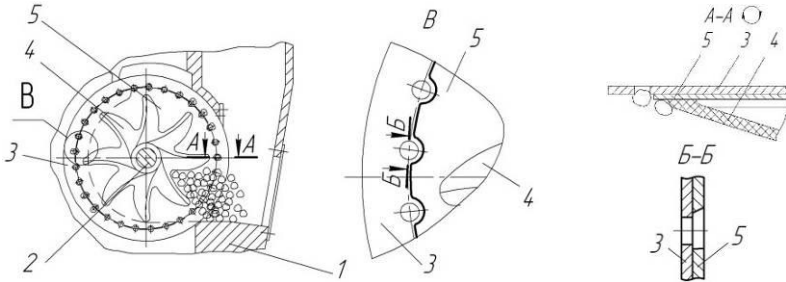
Пневмомеханічний висівний апарат: 1 – корпус; 2 – привідний вал; 3 – висівний диск; 4 – ворухила; 5 – додатковий диск
